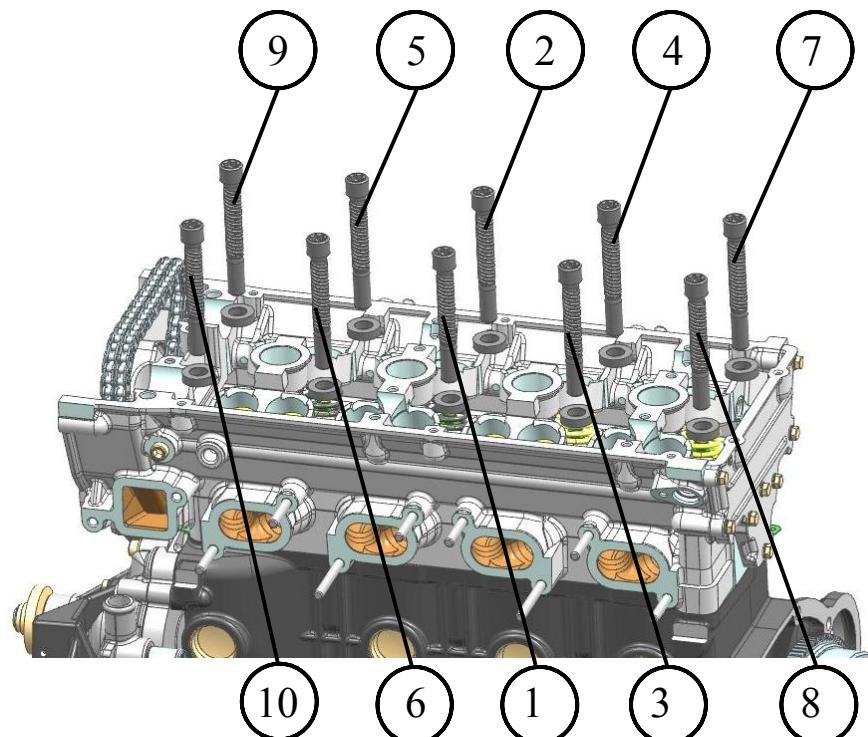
Последовательность затяжки болтов головки цилиндров двигателей с мягкой (из асбостального листа) прокладкой головки цилиндров
